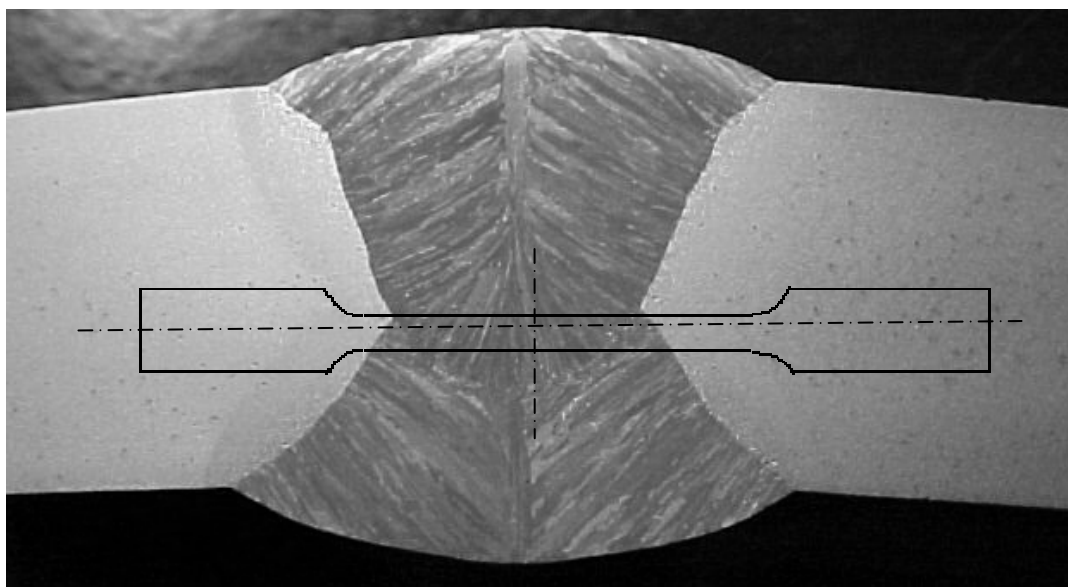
Corpo-de-prova cilíndrico de seção reduzida para ensaio de tração de solda
